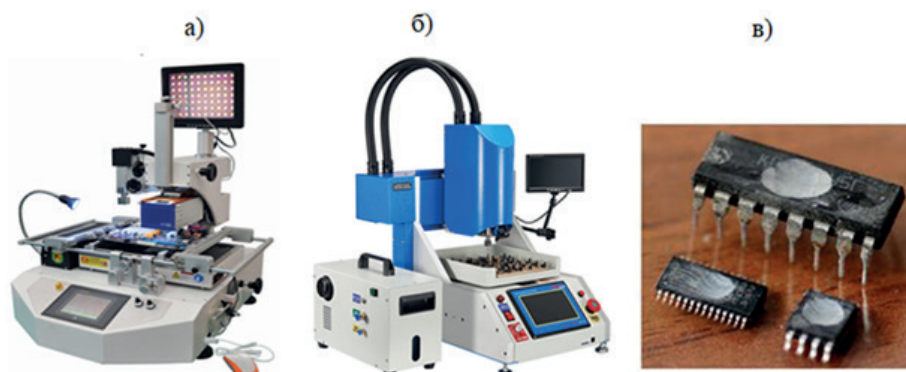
Установки демонтажа и механической декапсуляции ИМС: паяльная микровизионная станция RW-SV520 (а); прецизионный микровизионный фрезерно-шлифовальный станок LY-1001 (б); образцы ИМС, прошедшие фрезерную обработку (в).
